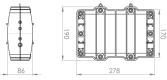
Vista exterior. Detalle frontal y lateral, con las dimensiones establecidas.
